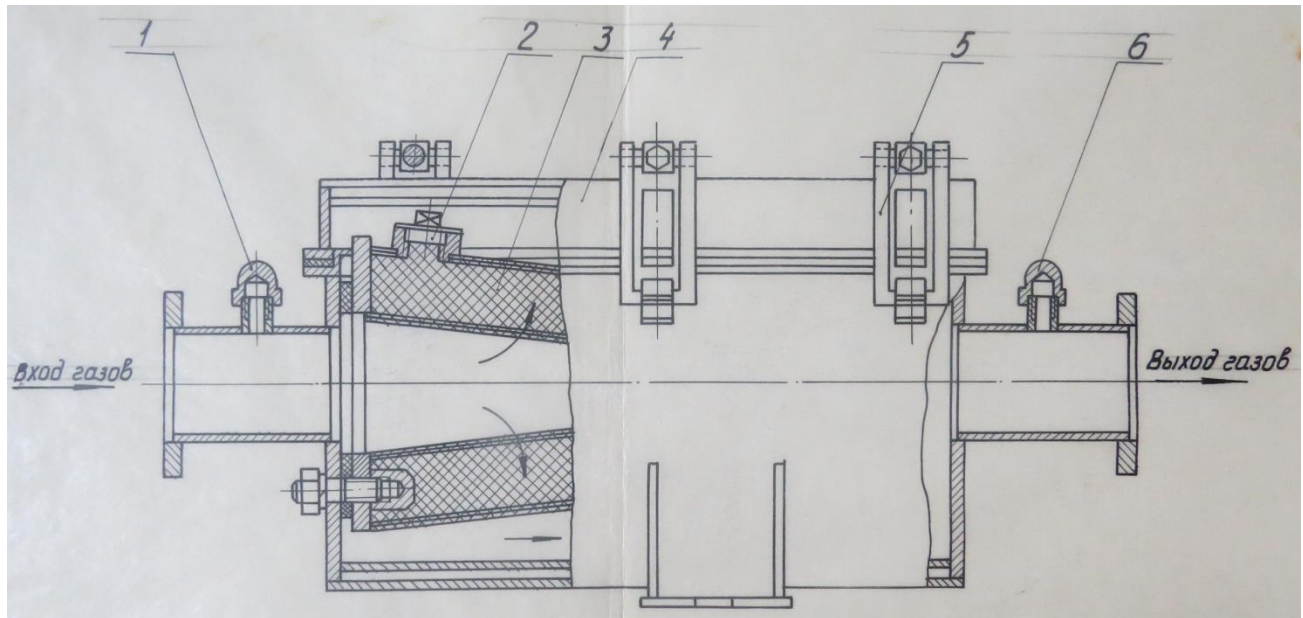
Схема каталітичного нейтралізатора вихлопних газів Д1-75:
